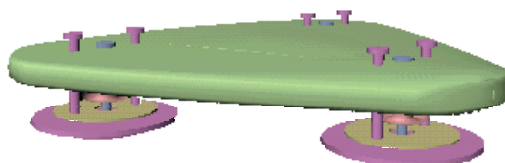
Vue du prototype virtuel du démonstrateur.
